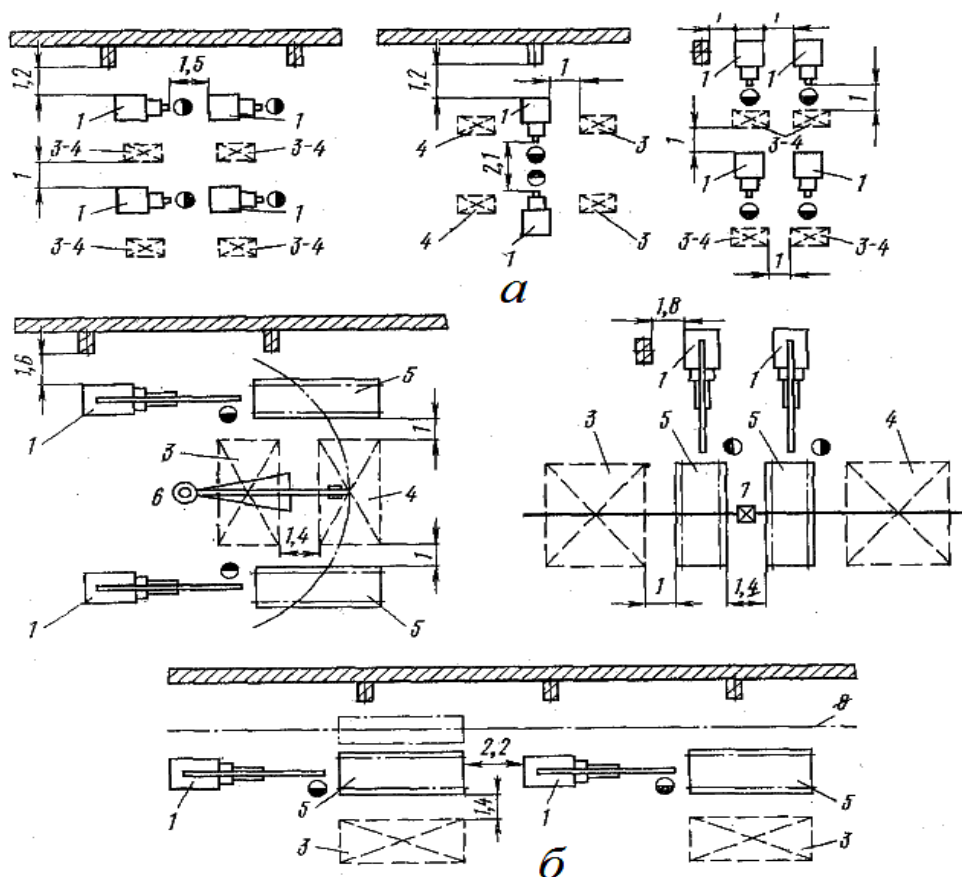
Приклади розташування машин для точкового і шовного зварювання при їх габаритних розмірах в плані:
